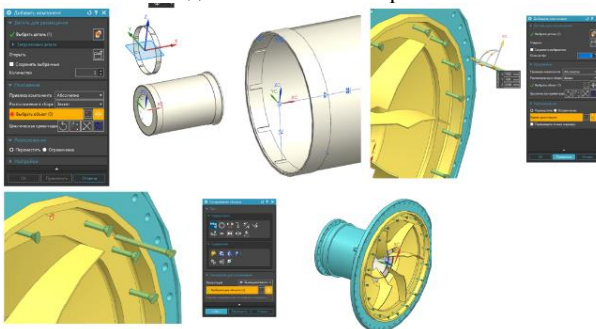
Сборка готовых деталей в области «Сопряжение сборки»
